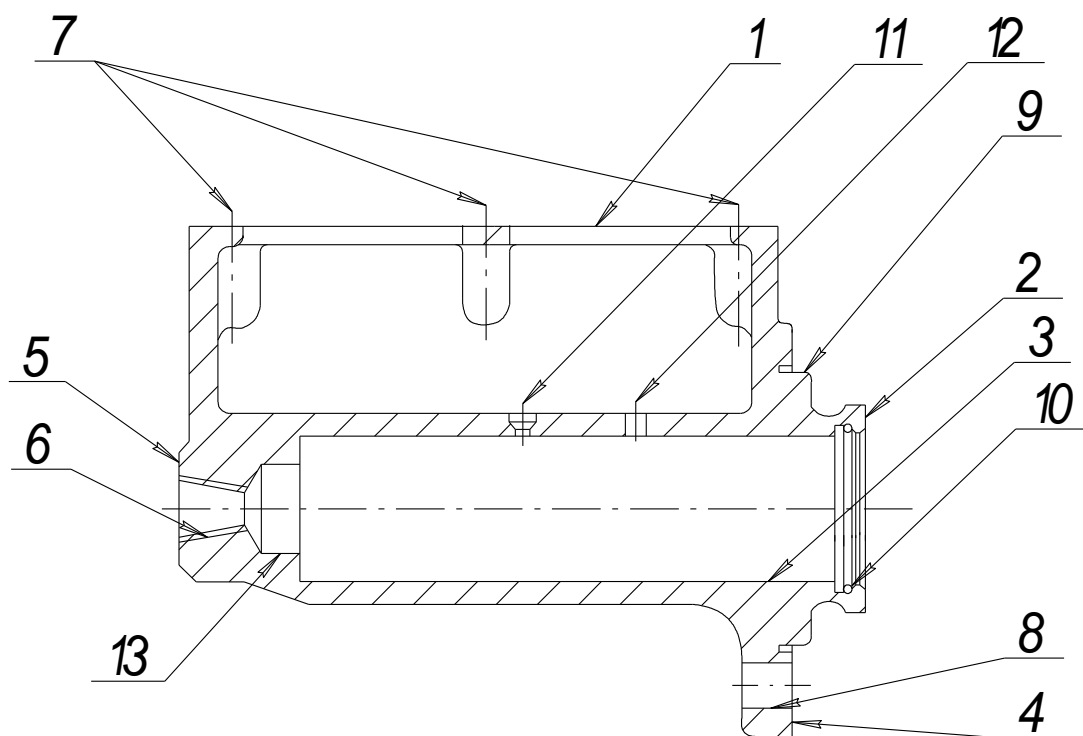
Эскиз корпуса тормозного гидроцилиндра
